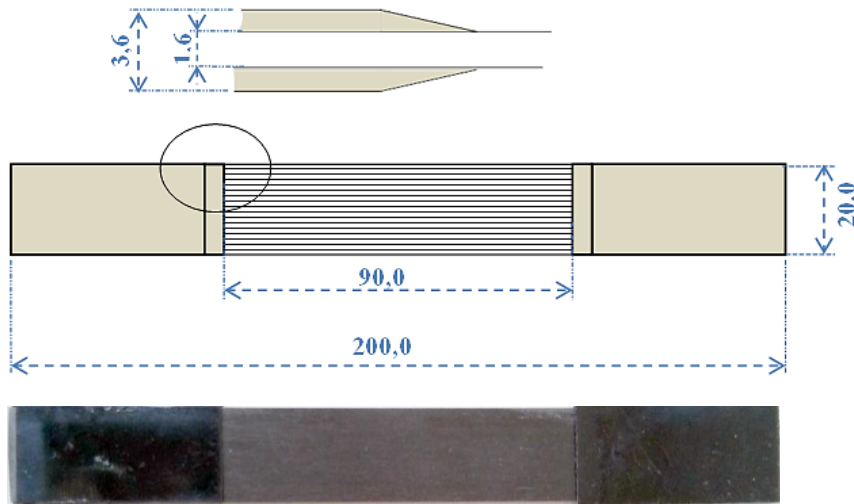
Dimensions et forme de l'éprouvette des stratifiés  $[0_2/\theta_2]_S$
